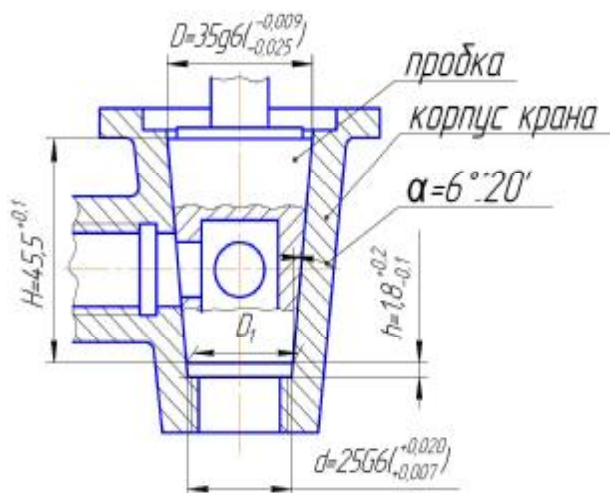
Схематизированный чертеж узла корпуса крана с пробкой
